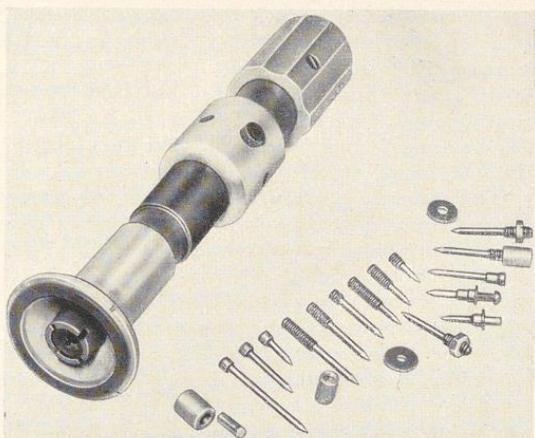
Rapidhammer mit Gewindegelenkbolzen
